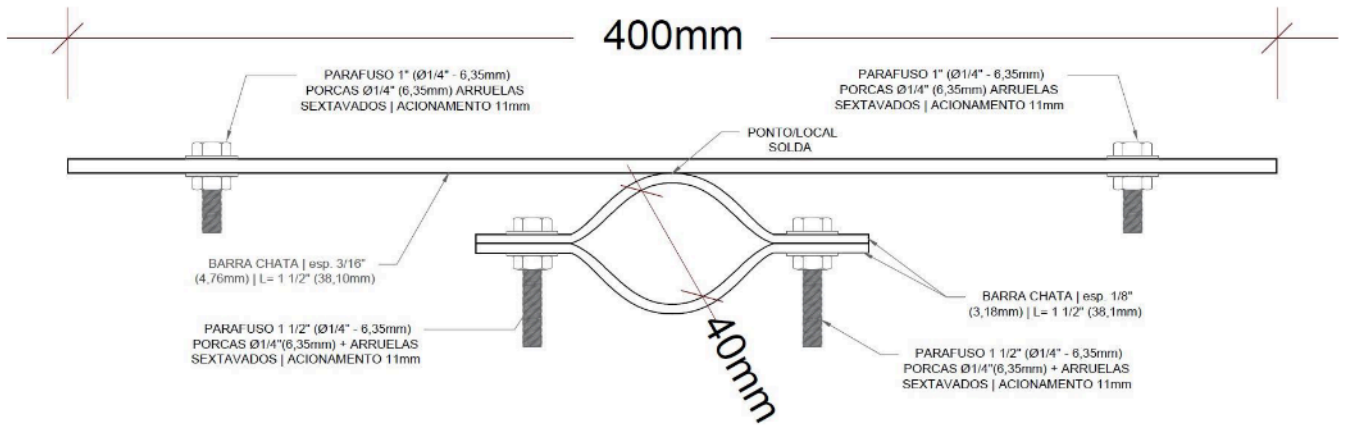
VISTA SUPERIOR DA ABRAÇADEIRA. FONTE: DET/SMST/PMBV
